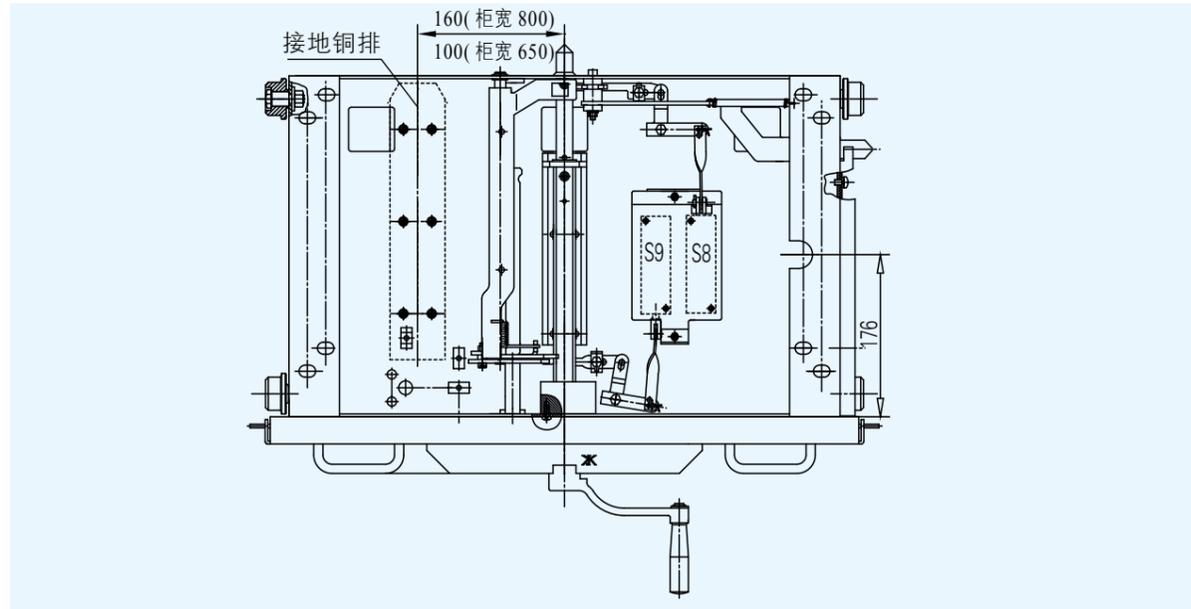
DPC-4-650/800 接地铜排位置尺寸图
